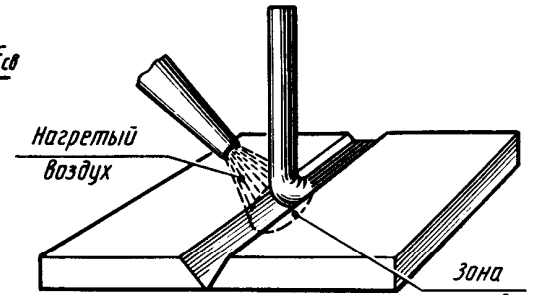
Схема сварки газовым теплоносителем с присадочным материалом
